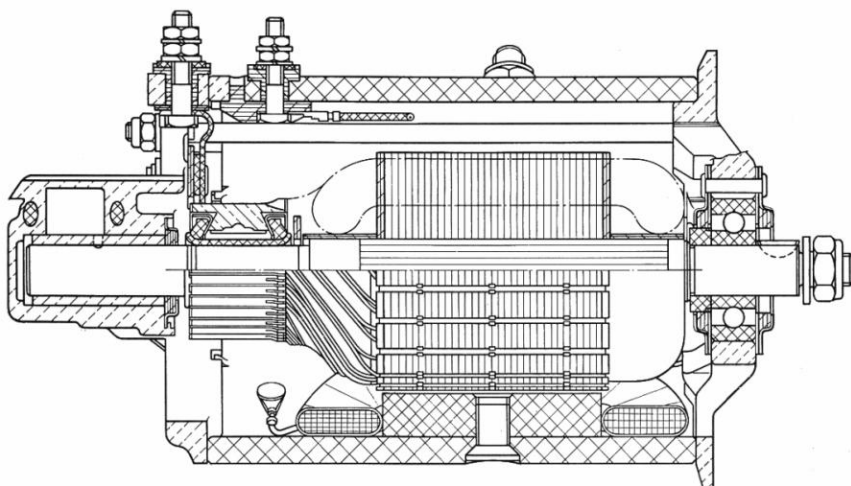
Längsschnitt durch die Lichtmaschine.
